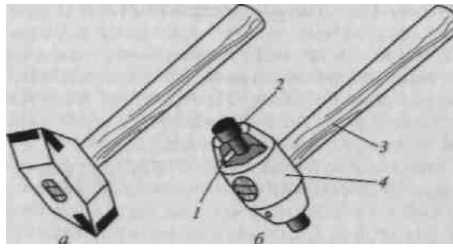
Молотки с мягкими вставками: а - с призматической; б - с цилиндрической: 1 - штифт; 2 -боек; 3 - рукоятка; 4 - корпус
